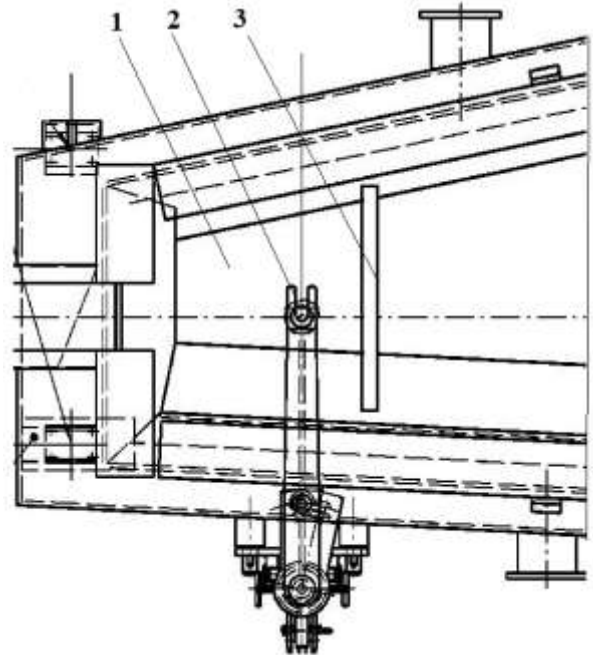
Конструкции оборудования разливной камеры ковша МНЛЗ:
